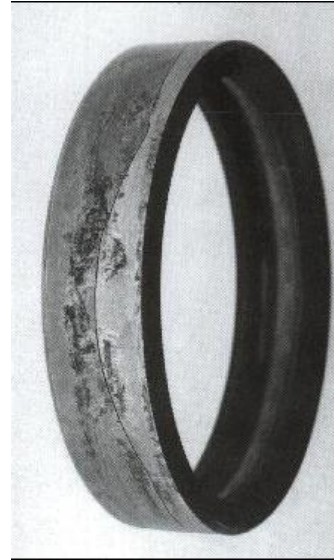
Rotura longitudinal de un aro exterior de rodamiento rígido de bolas, con corrosión de contacto.
